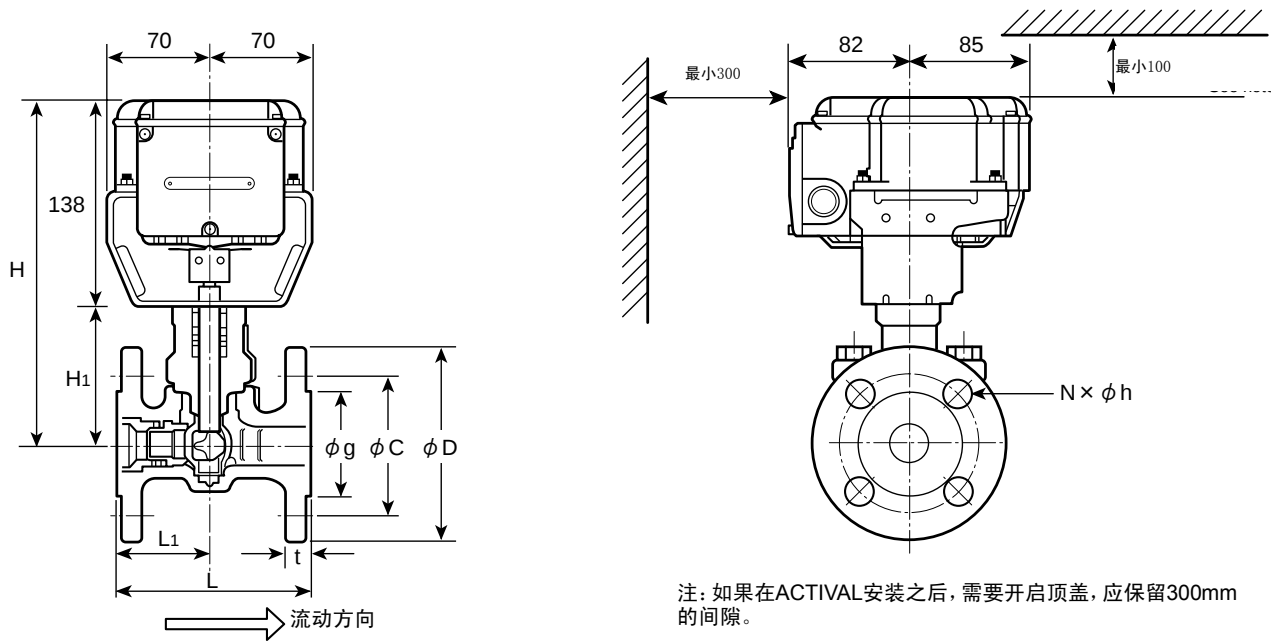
尺寸 (mm): 阀体 (JIS SCS13A)
